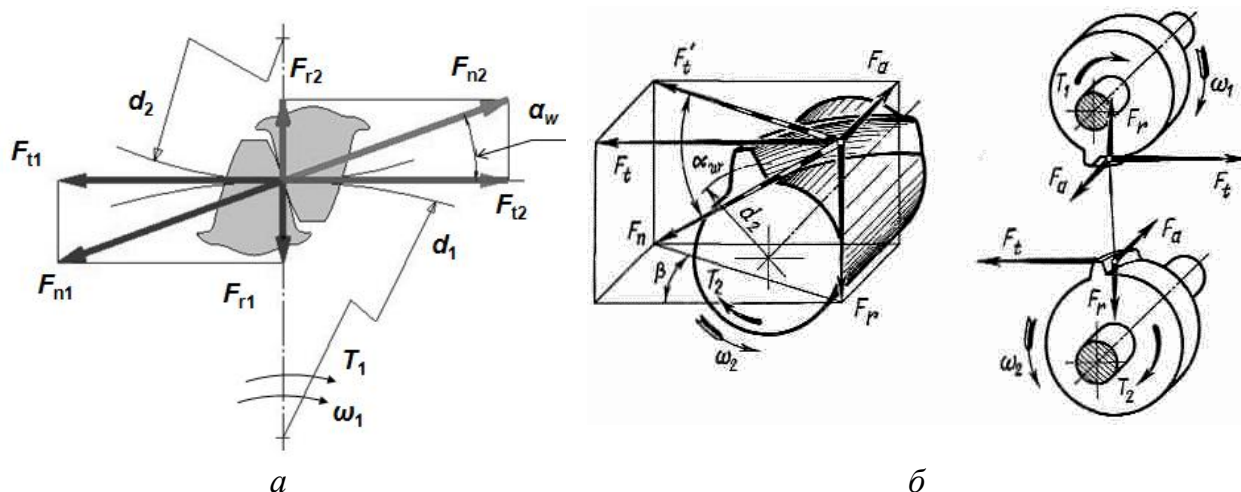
Схема сил, действующих в цилиндрической зубчатой передаче:
